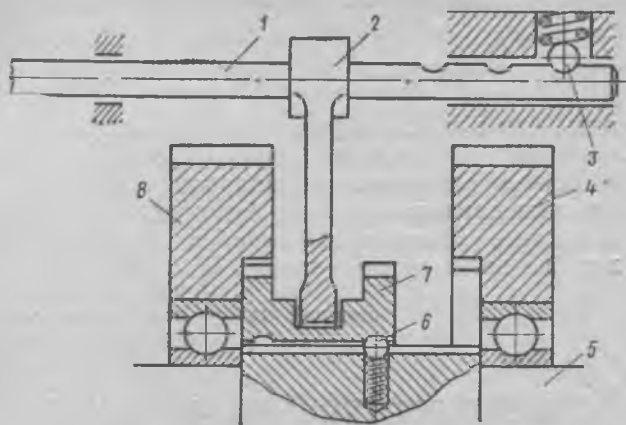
Дополнительная фиксация муфты реверса тепловоза ТУ4: 1 — валик; 2 — вилка переключения; 3 — стопорный шарик; 4 — шестерня, ведомая на передний ход; 5 — вал реверса; 6 — дополнительный стопорный шарик; 7 — муфта реверса; 8 — шестерня, ведомая на задний ход
